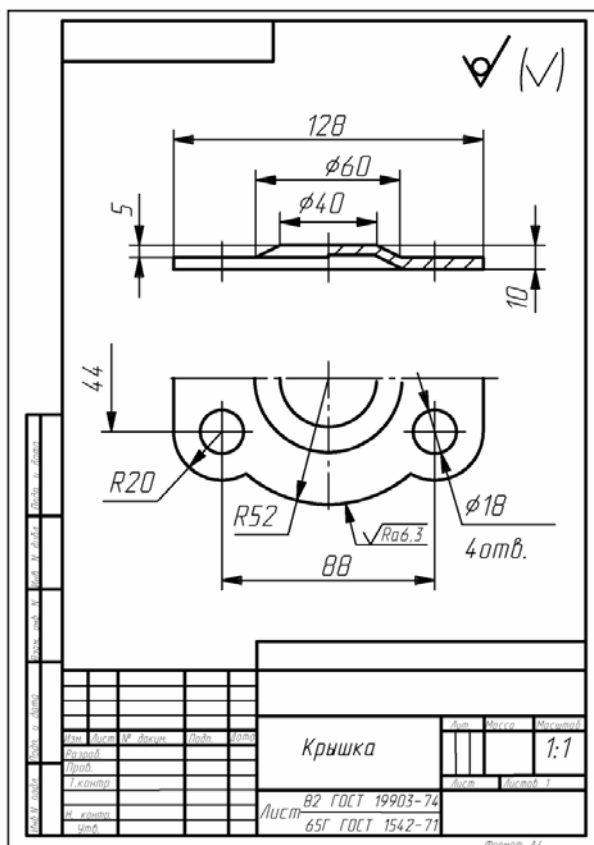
Приклад кресленника деталі з листового матеріалу
